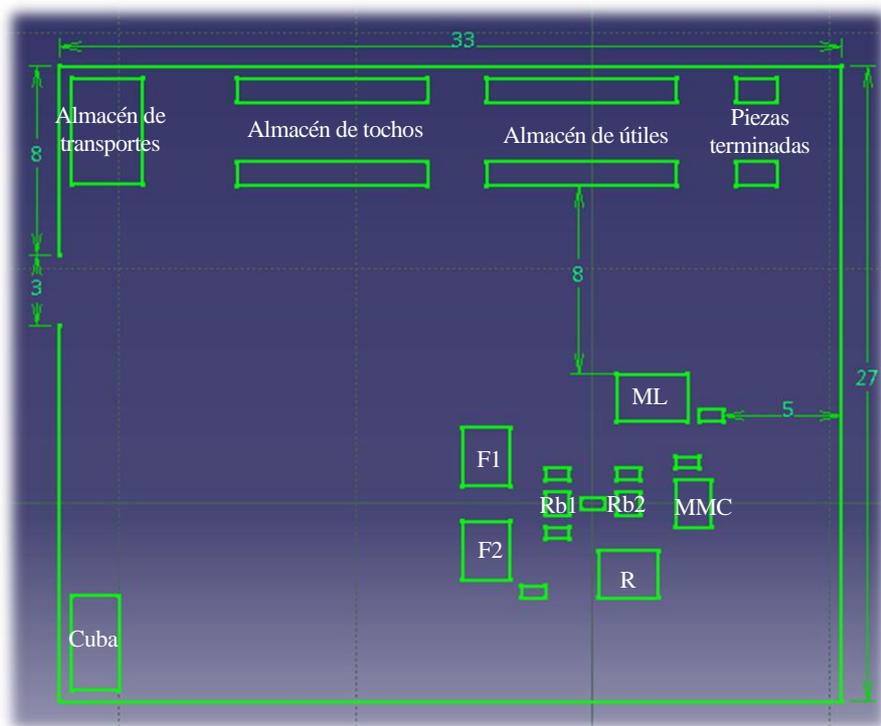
14. Situación de la célula centrada en robots en la planta de fabricación.
